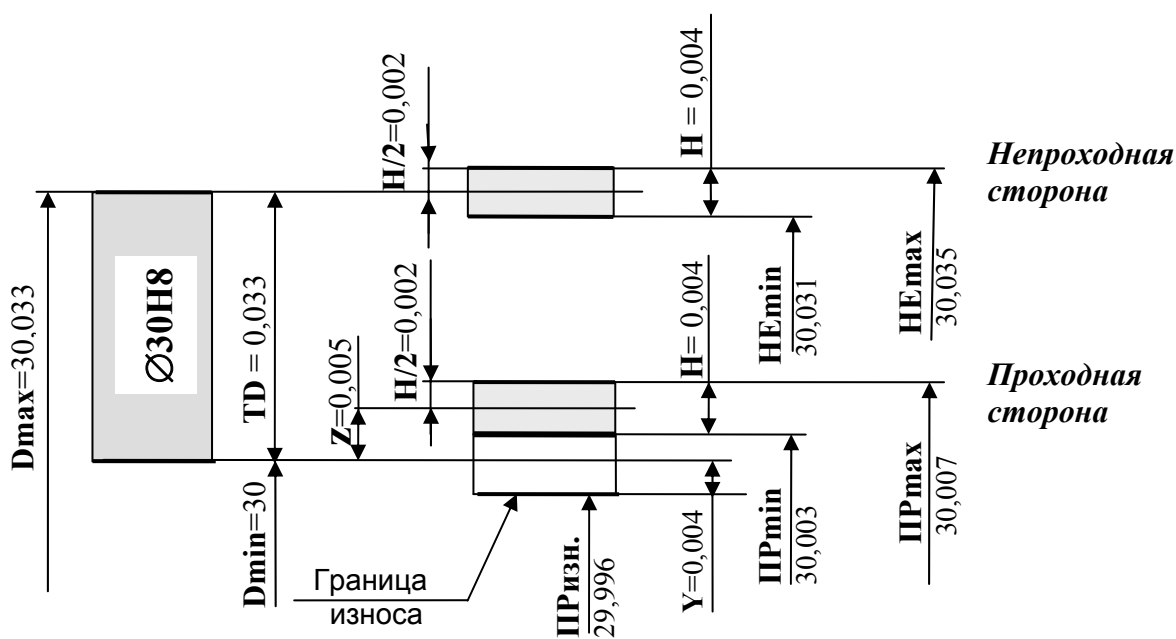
Схема расположения полей допусков отверстия ПР и НЕ сторон калибра пробки
